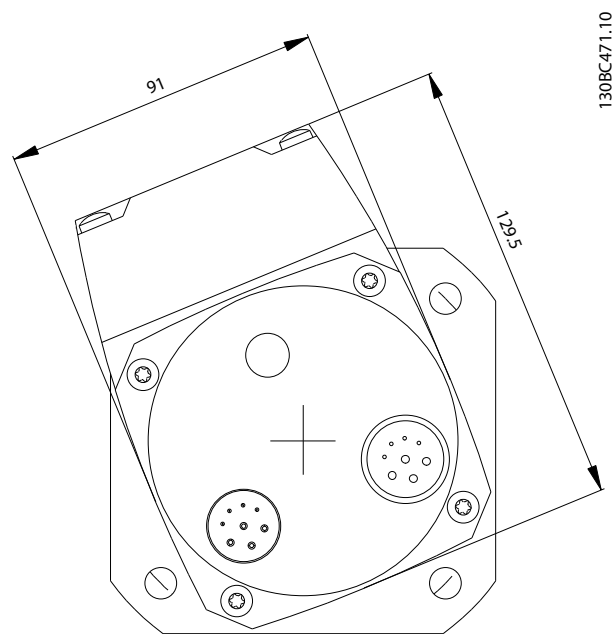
Rückansicht: Servomotor mit IEC Flansch und Bremse
